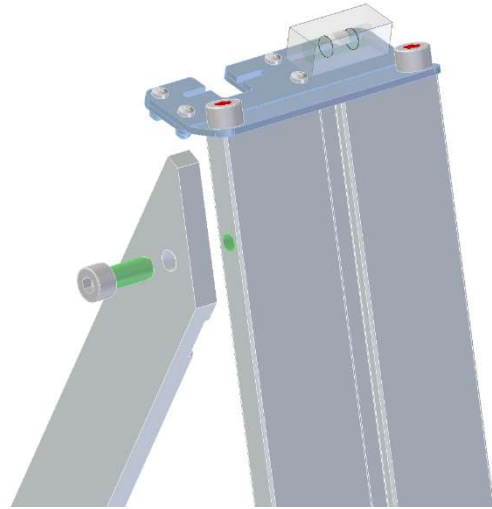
Montaje del puntal de apoyo en el caballete de soporte
